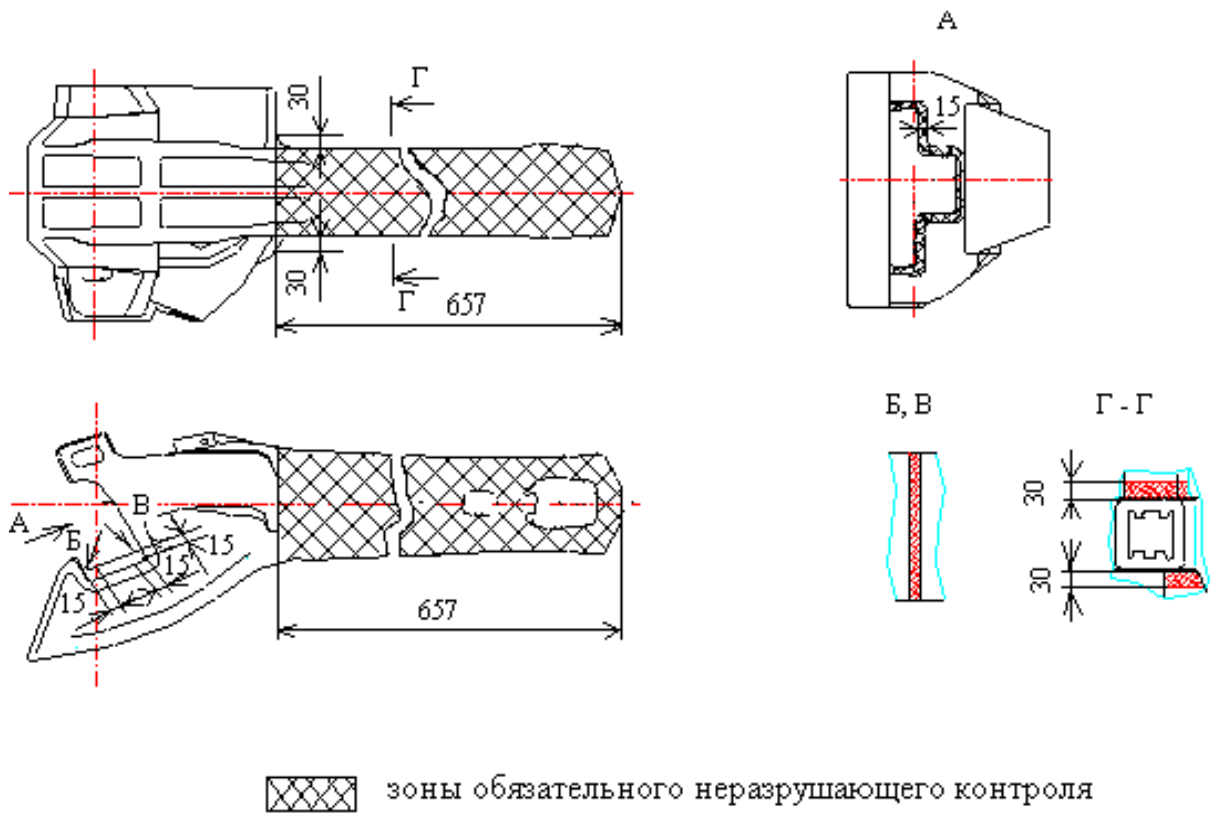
Зоны неразрушающего контроля на корпусе автосцепки СА-3М
